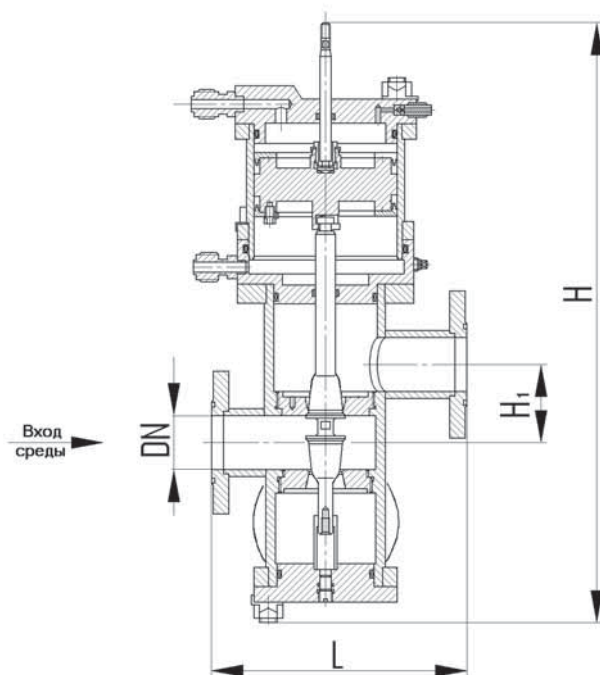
Клапан регулирующий проходной фланцевый
